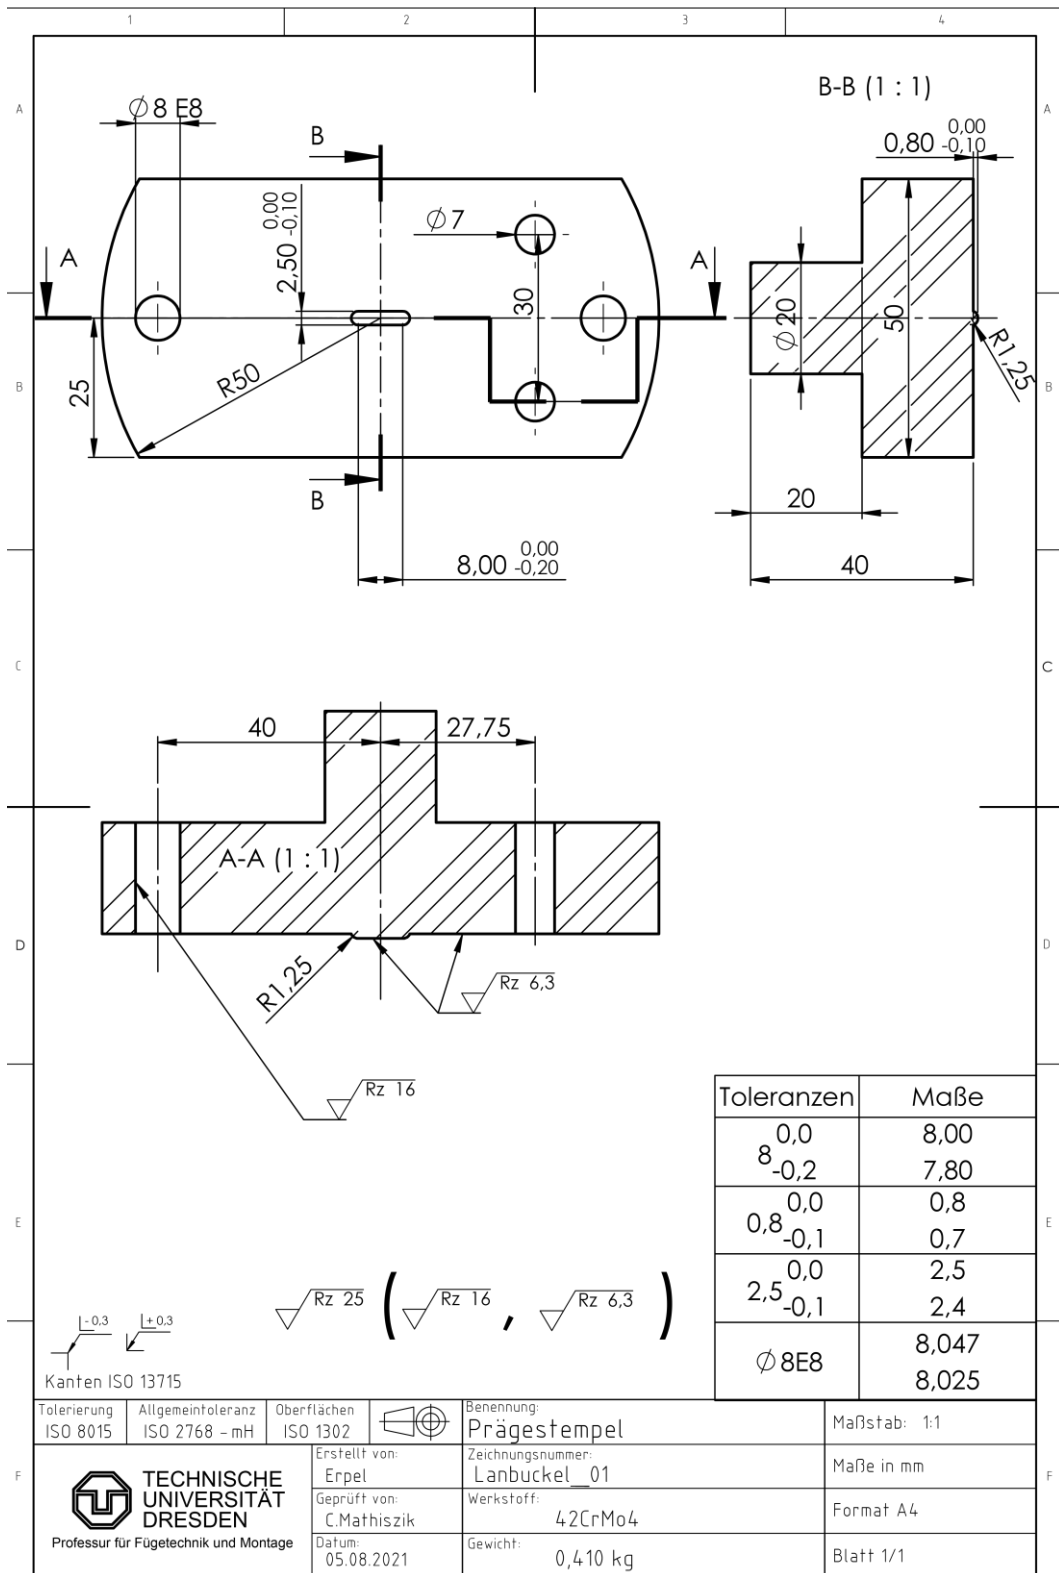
Technische Zeichnung des Stempelwerkzeugs der Prägevorrichtung
